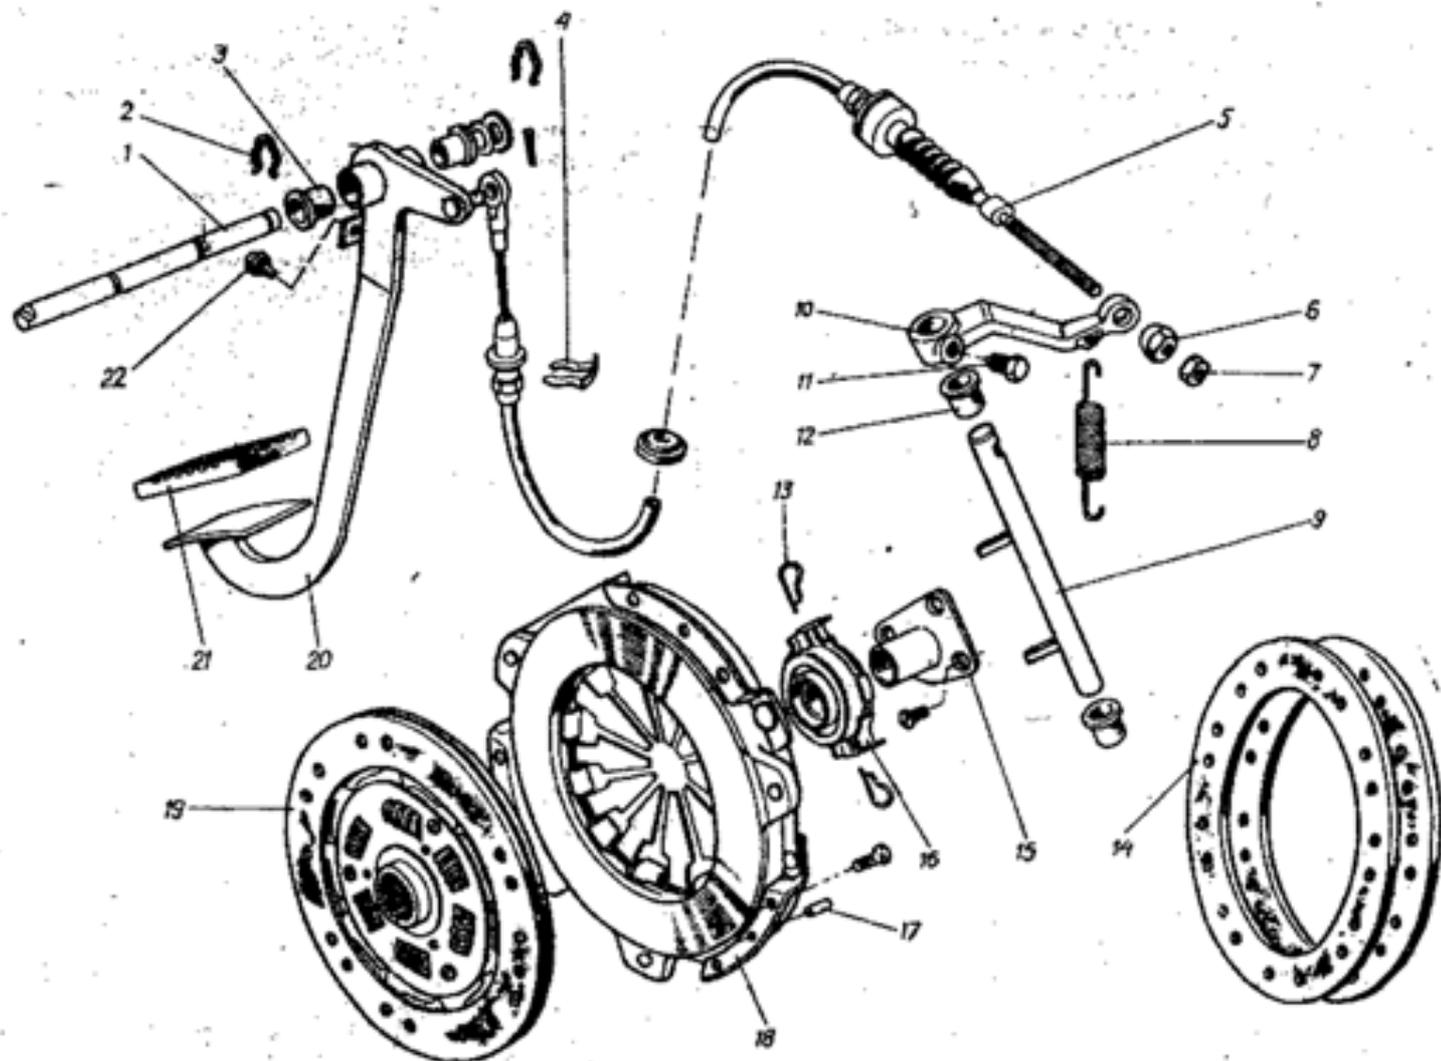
Детали механизма сцепления и его привода. 1 - ось педалей; 2 - защелка; 3 - втулка педали; 4 - фиксатор; 5 - трос в сборе; 6 - гайка регулировочная; 7 - контргайка; 8 - пружина оттяжная рычага; 9 - вилка; 10 - рычаг; 11 - стопор; 12 - втулка вилки; 13 - звено соединительное; 14 - накладка фрикционная; 15 - фланец; 16 - подшипник в сборе; 17 - штифт; 18 - диск нажимной; 19 - диск ведомый; 20 - педаль сцепления; 21 - накладка; 22 - буфер резиновый
